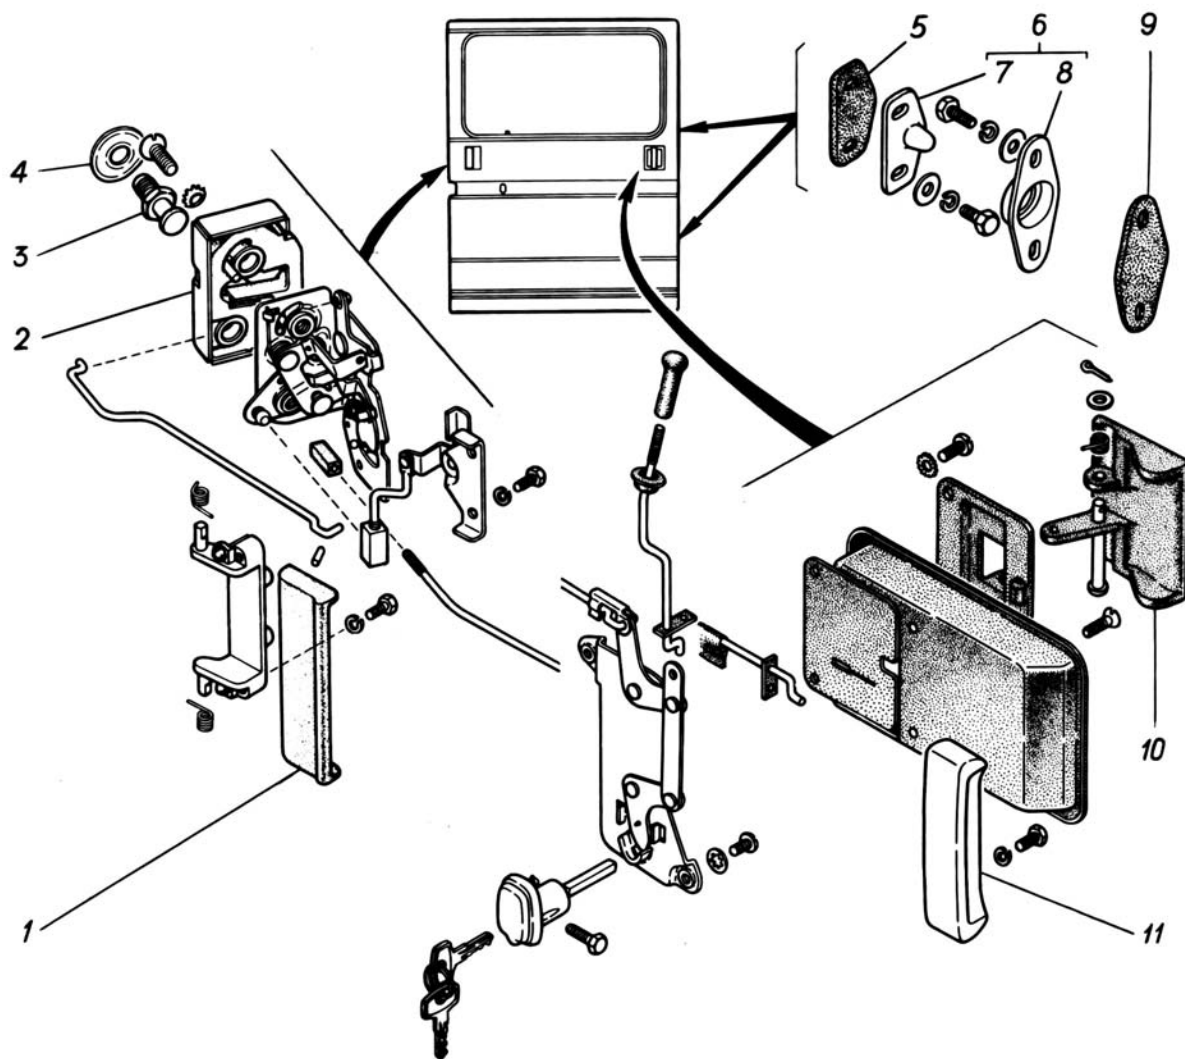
Механизм фиксации и запираения боковой двери: 1 - задняя наружная ручка привода замка; 2 - запорный механизм замка; 3 - шип замка; 4 - шайба шипа; 5 и 9 - регулировочные прокладки; 6 - фиксатор двери; 7 - шип фиксатора; 8 - корпус фиксатора; 10 - внутренняя ручка привода замка; 11 - передняя наружная ручка
